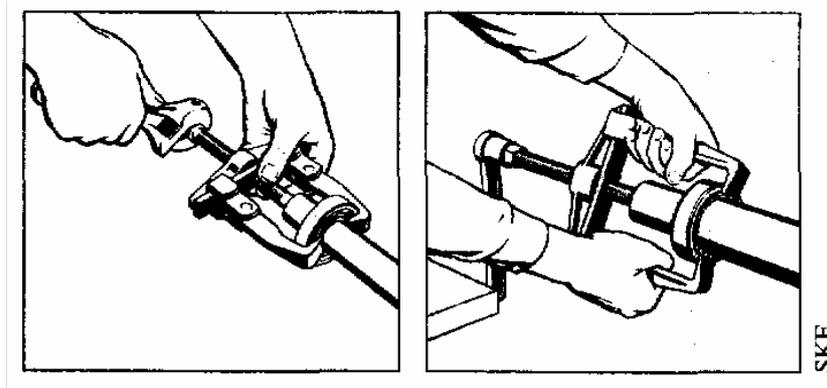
Extraction d'un roulement à billes monté serré sur arbre
